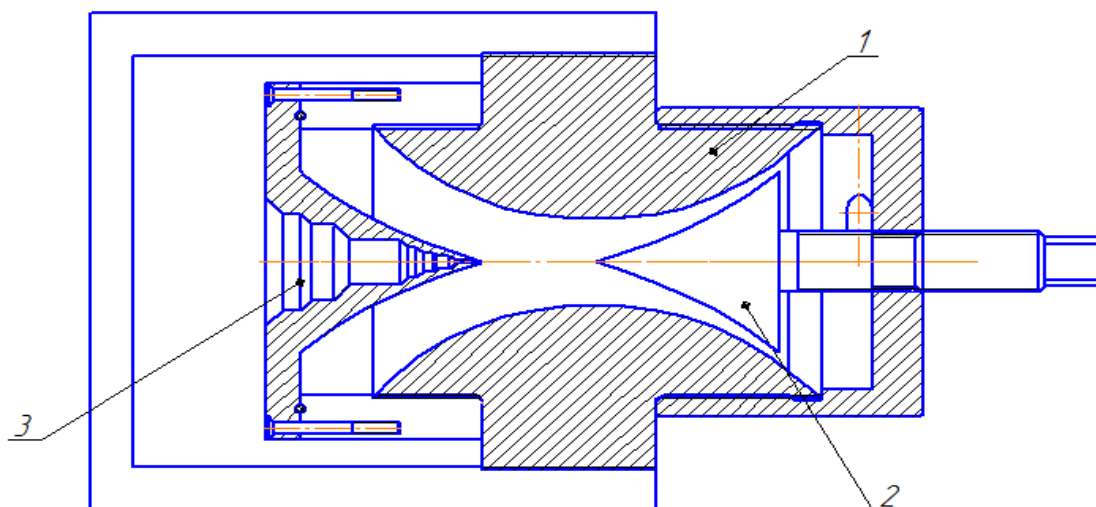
Общий вид гомогенизирующего устройства с камерой энергетического разделения гиперболической формы: 1 – корпус камеры, 2 – клапан, 3 – устройство подачи продукта
